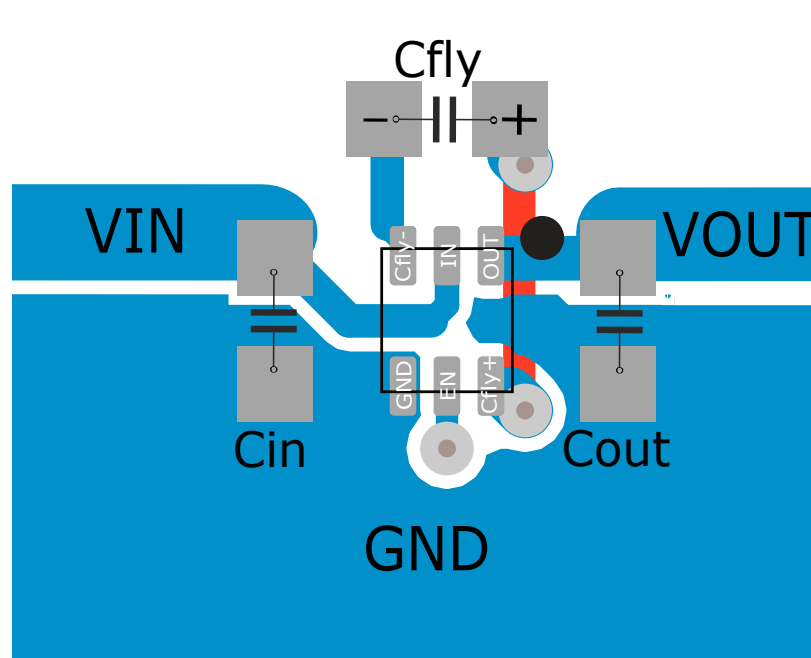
TPS60800-Q1 的建议 PCB 布局 (顶层)
